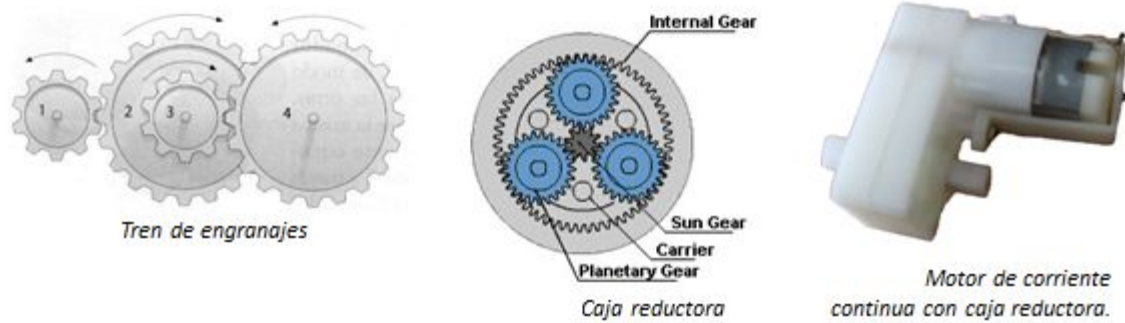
diagrama que indica cómo está construido un motor con caja de engranajes.
